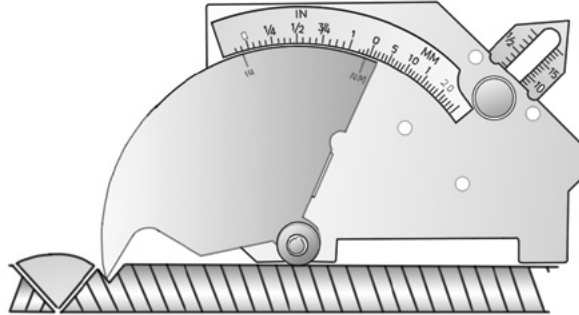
Tolok kimpal jenis *Cam Bridge
